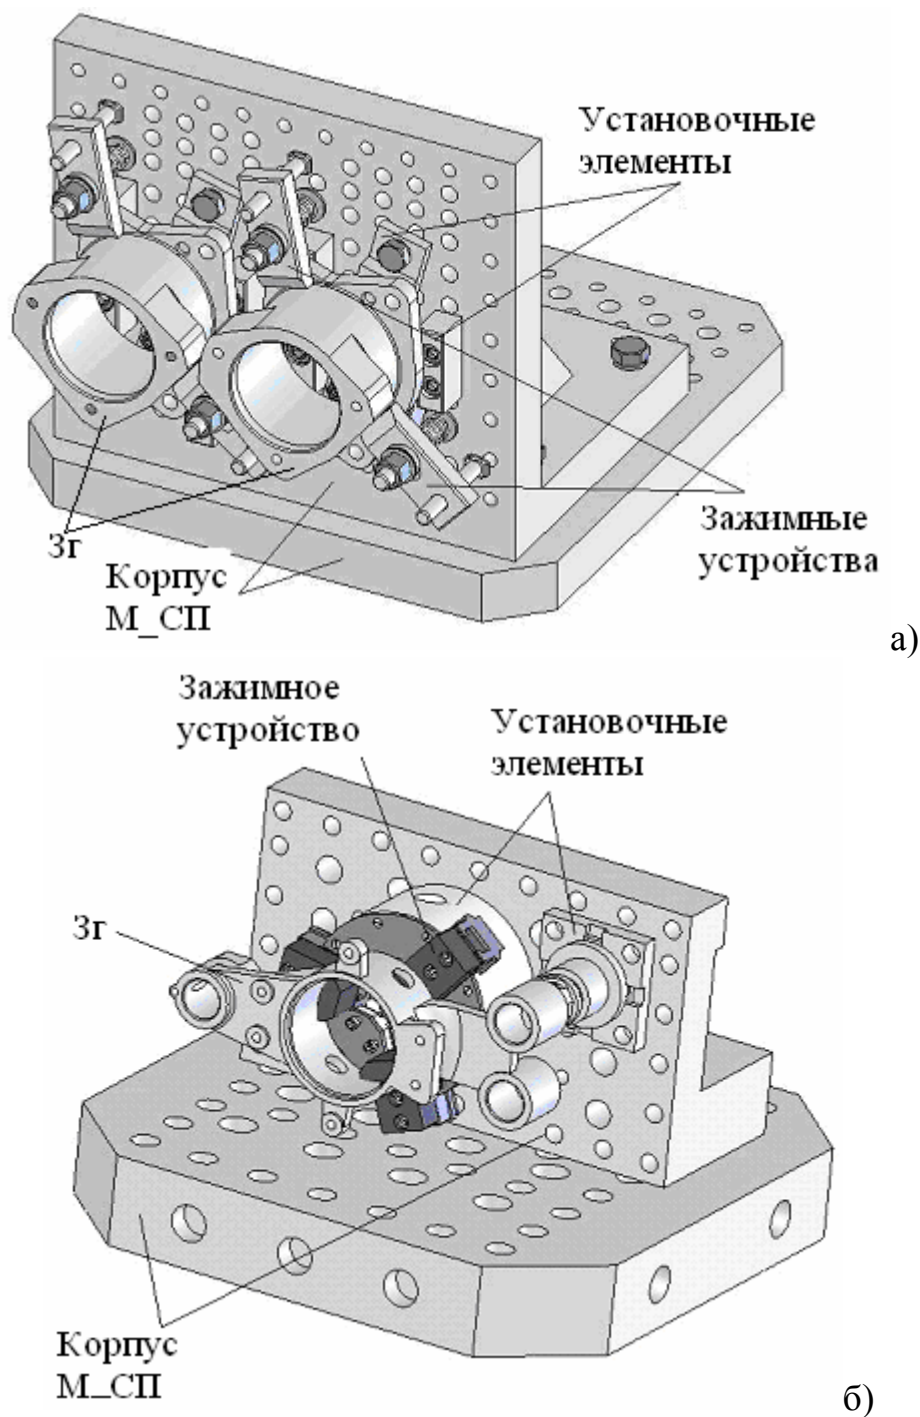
Модели приспособлений модульного типа для установки и закрепления деталей типа «Корпус»
